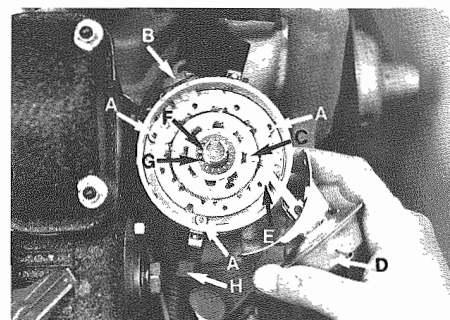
A - Viti di fissaggio statore - Stator fixing screws
